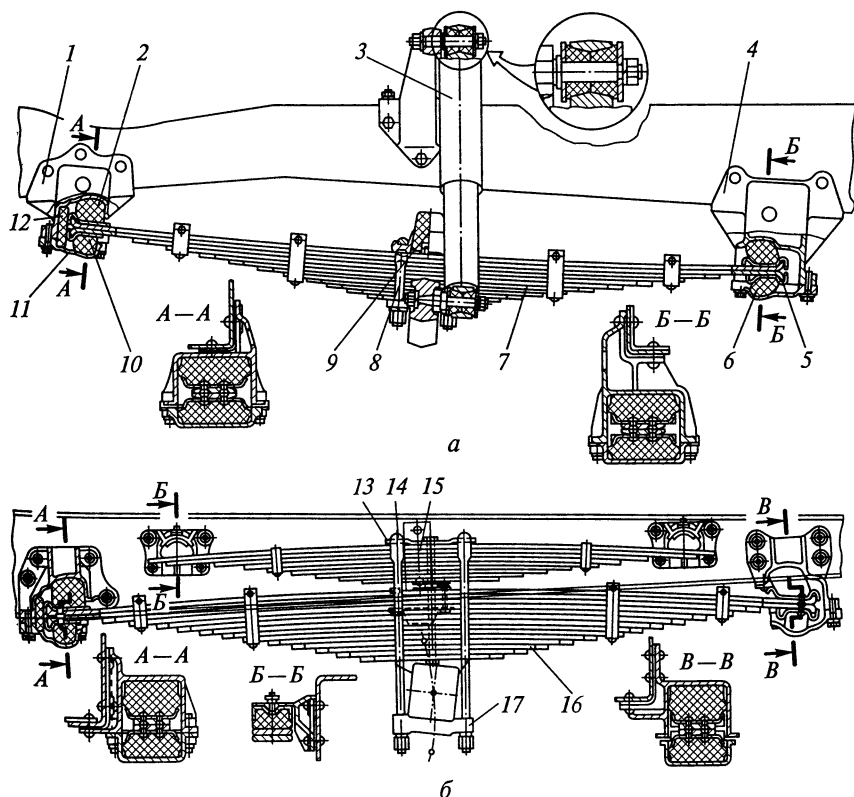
Передняя (а) и задняя (б) подвески грузовых автомобилей ГАЗ: 1, 4 — кронштейны; 2, 11, 12 — опоры; 3 — амортизатор; 5, 10 — чашки; 6 — крышка; 7, 16 — рессоры; 8, 14 — стремрянки; 9 — буфер; 13, 17 — накладки; 15 — подрессорник
